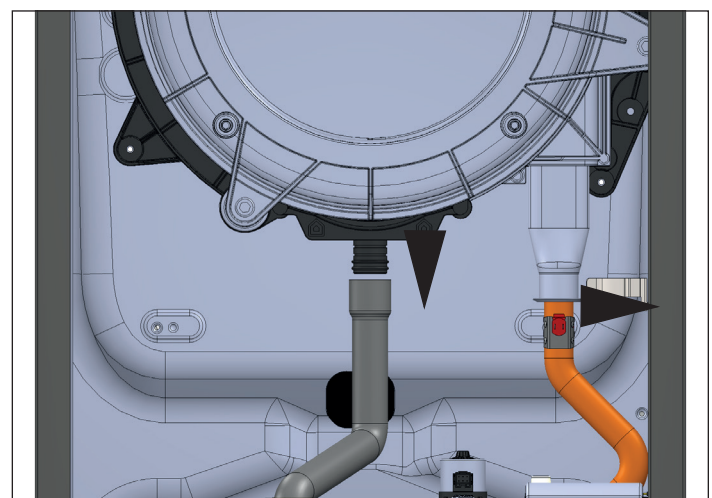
Retrait du conduit des condensats et du conduit de retour du chauffage central
